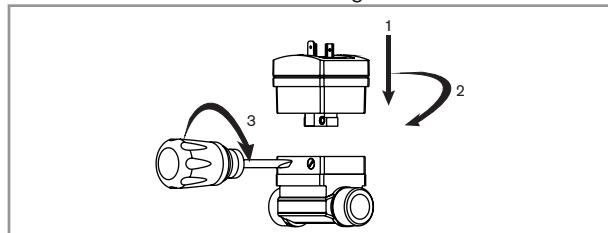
Montage des SE30 Ex auf ein Fitting S030
